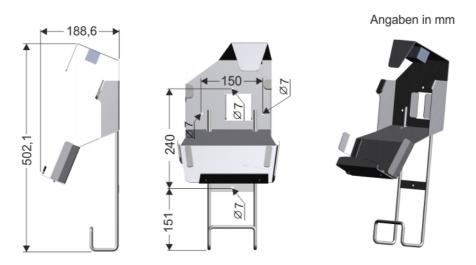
Medidas y cotas de barrenado para el soporte del smartPAD
